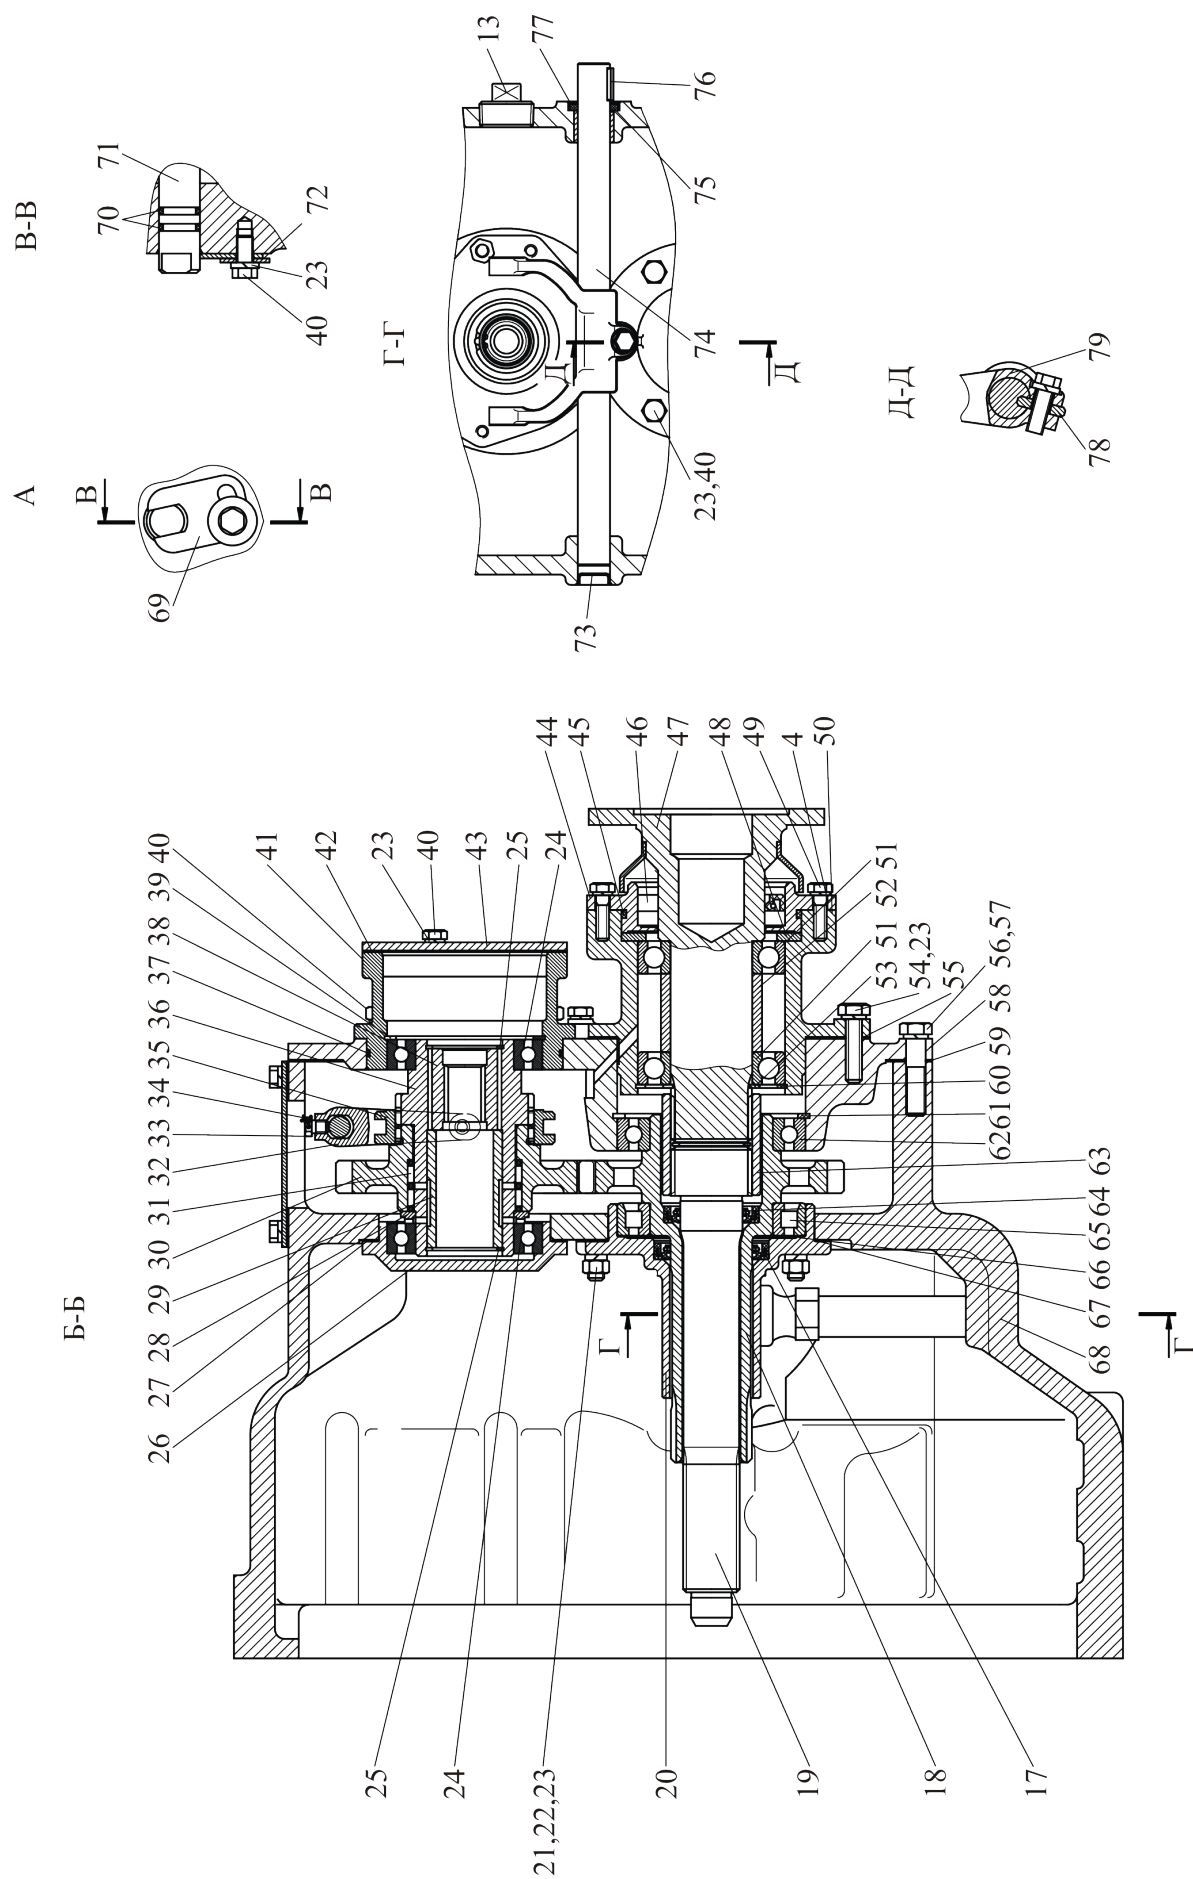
(лист 2 из 2) – Корпус сцепления
